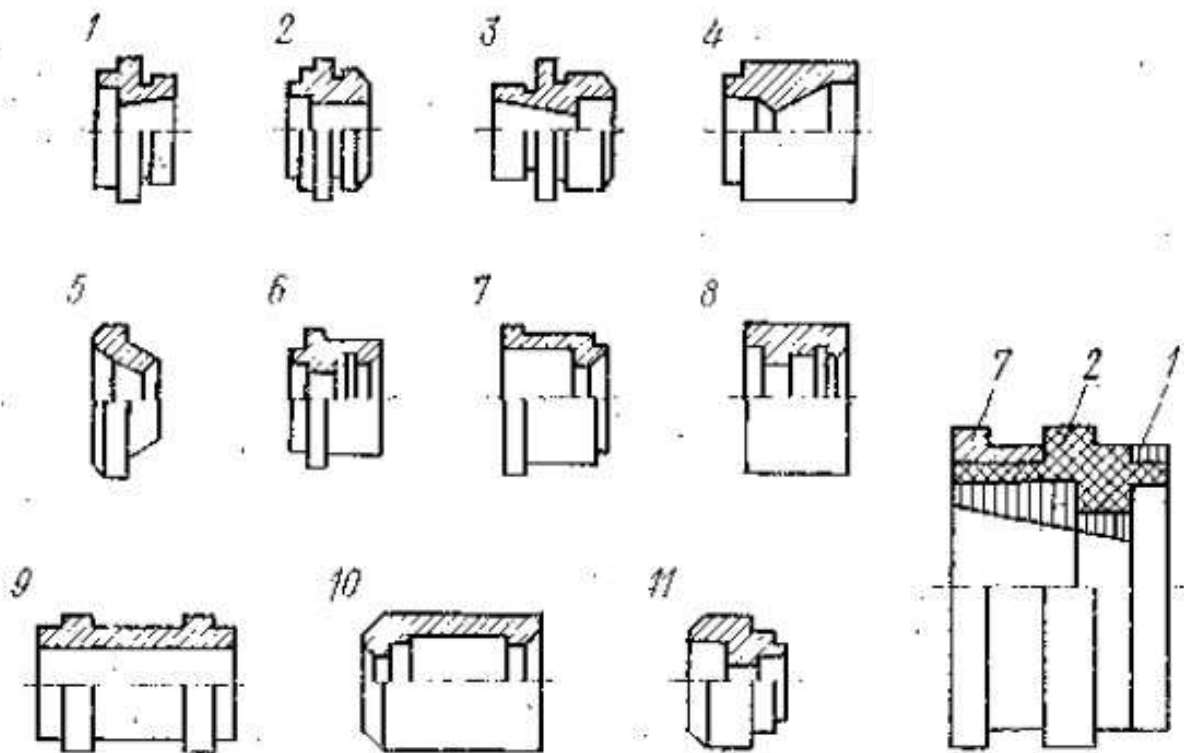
Схема побудови комплексної деталі (типу втулок)
